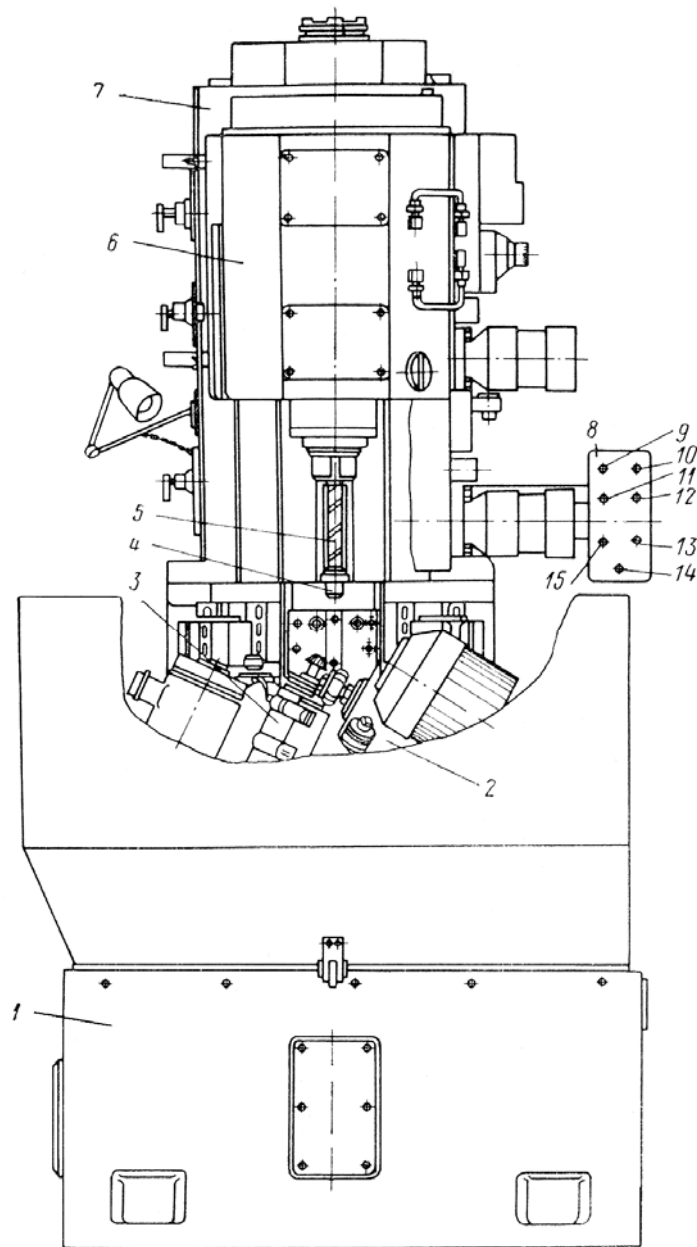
Общий вид специального сверлофрезерного полуавтомата мод. 6В-4М:
